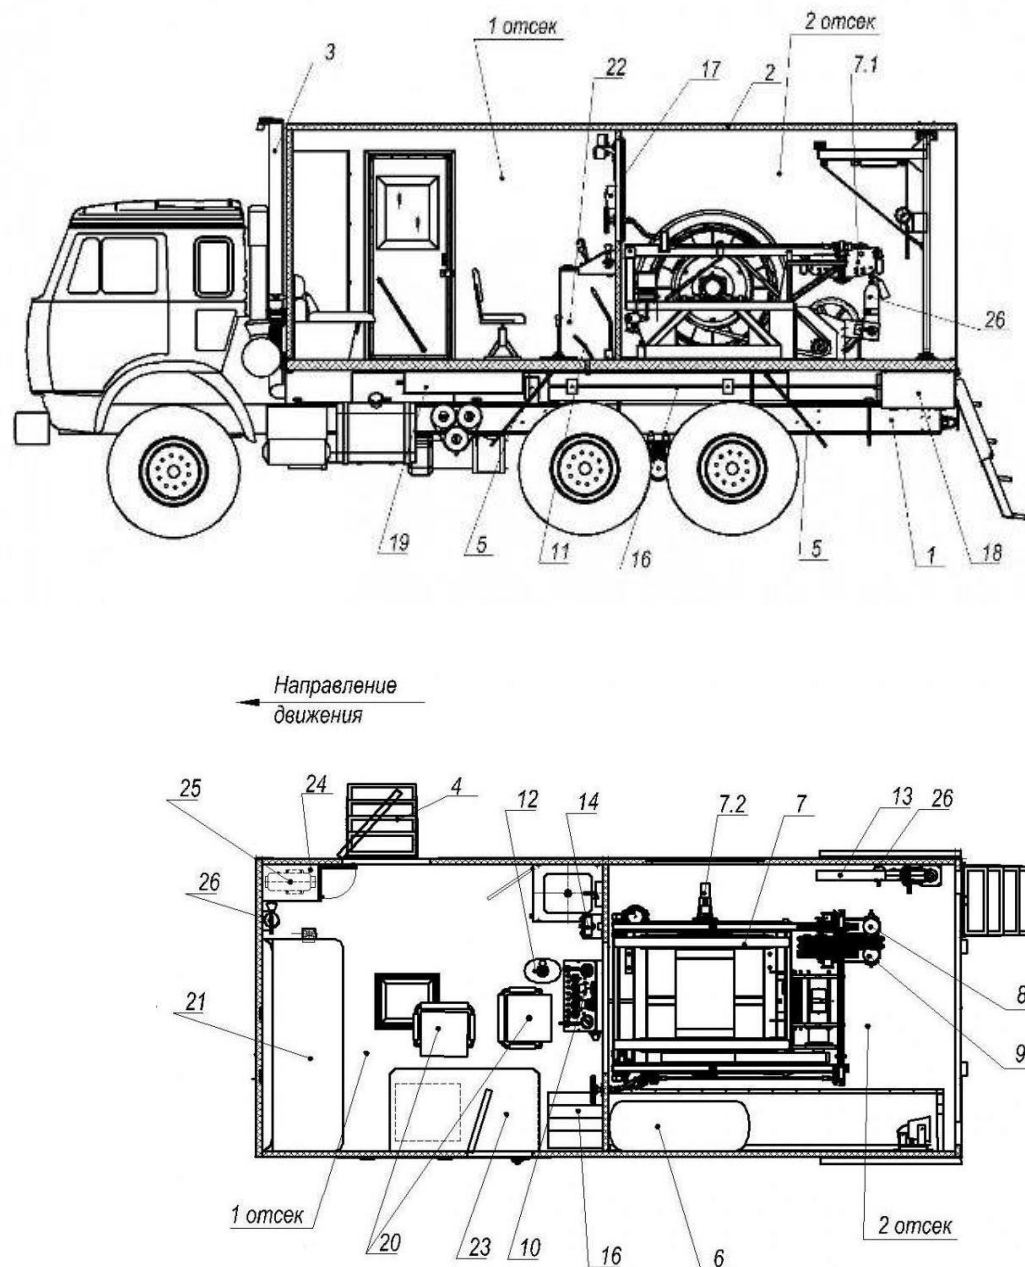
Каротажный подъемник, схема размещения оборудования:
